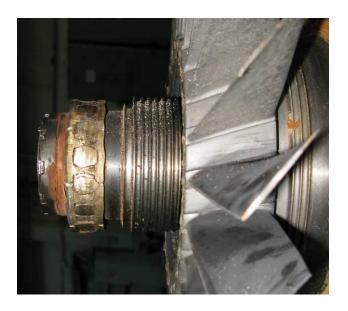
Вид разрушенного роликового подшипника передней опоры ротора компрессора.
